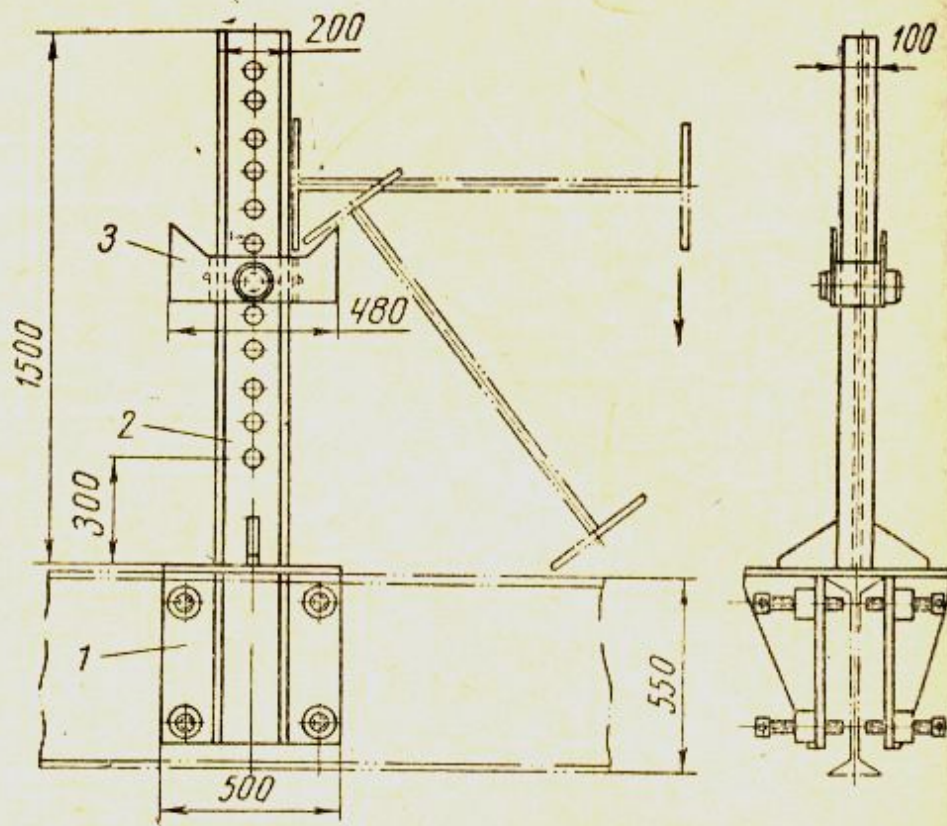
Переносная стойка для поддержки свариваемых конструкций:
